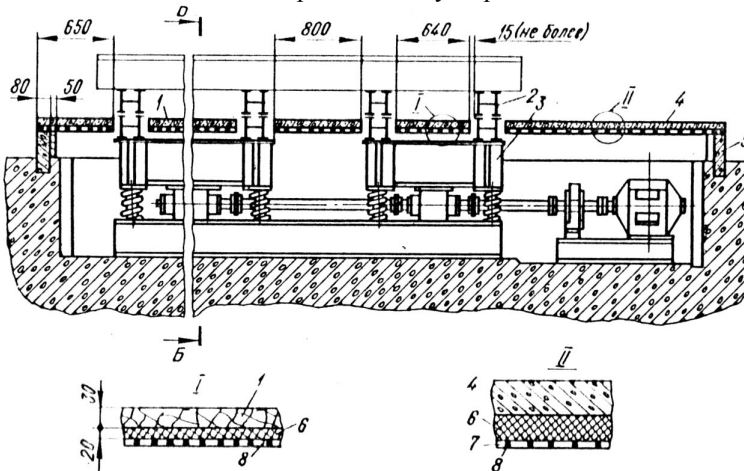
Звукоизолирующие укрытия для виброплощадки СМ-476Б:
